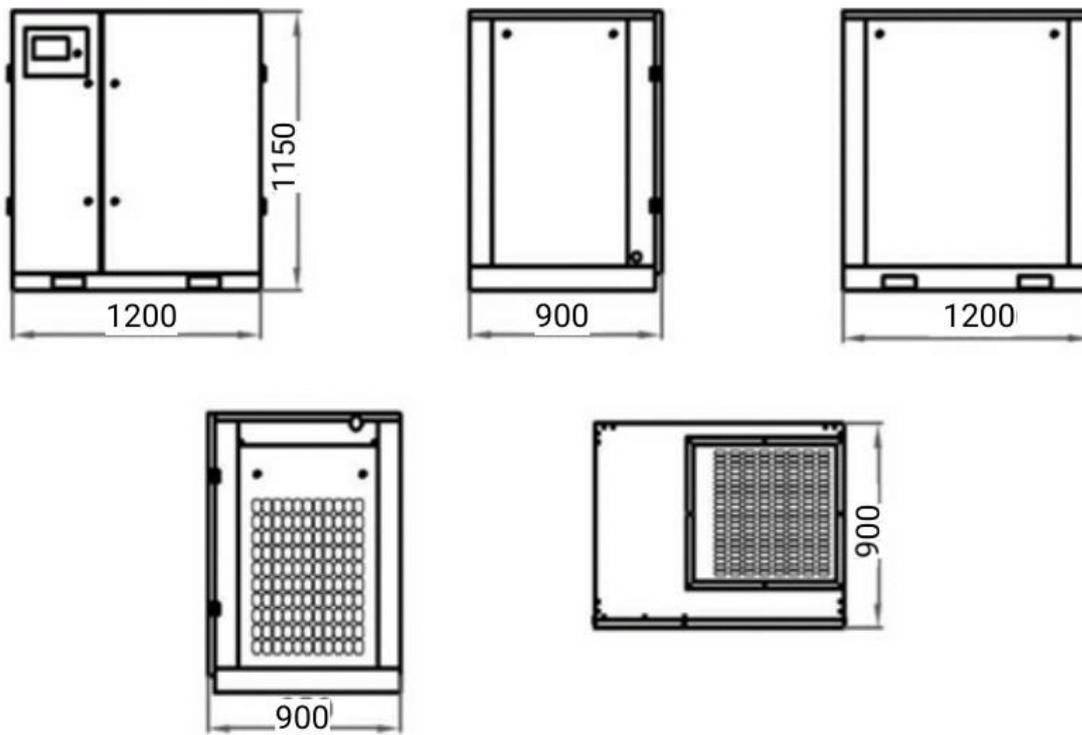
Габаритные размеры компрессоров BRM-22A
